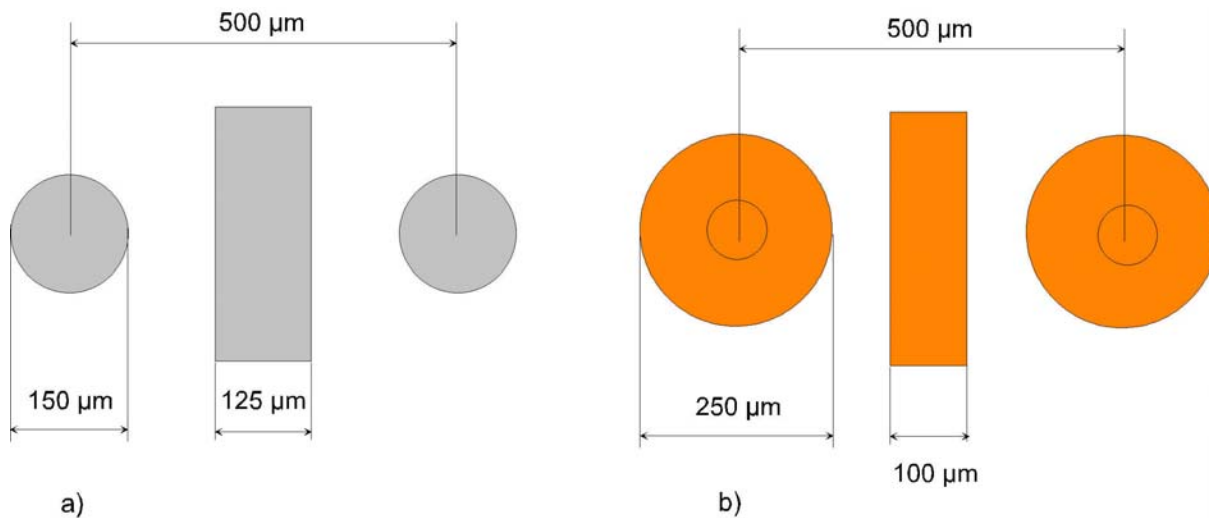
Entflechtung des CSP über a) LTCC b) PCB
